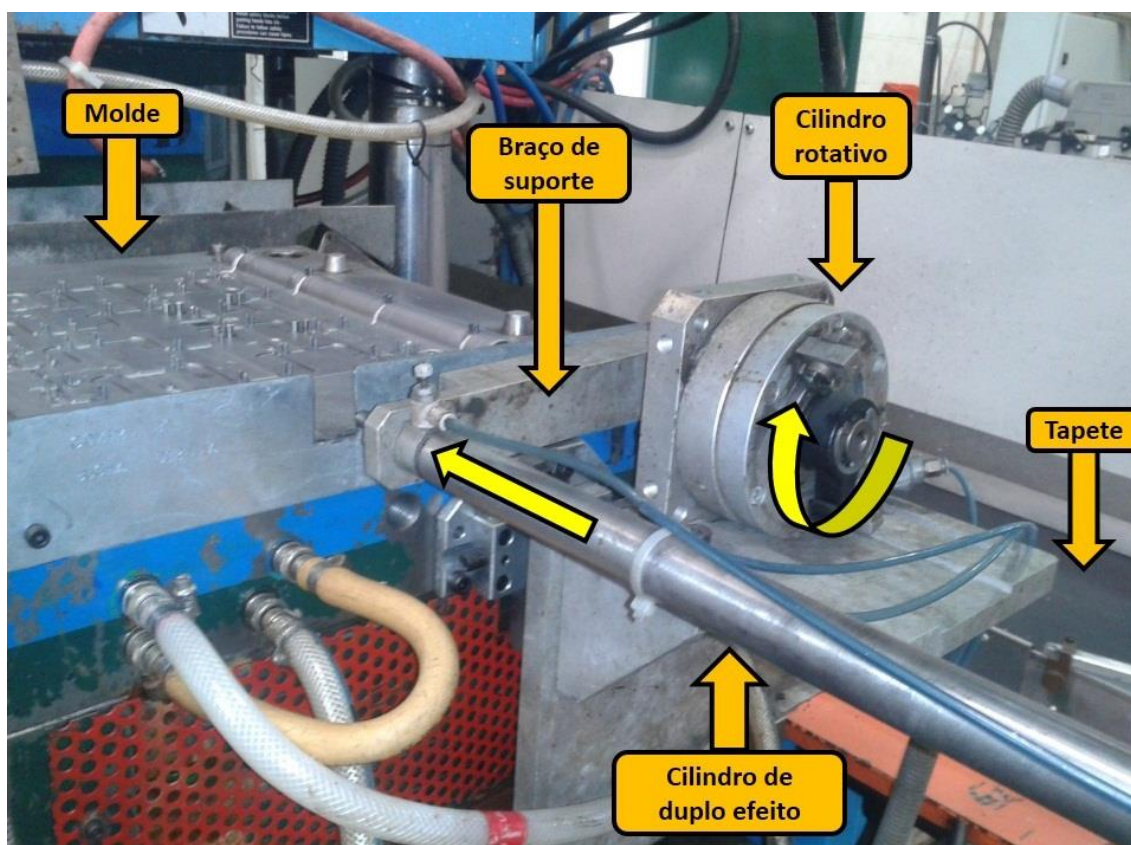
Componentes e movimentos da extração por cilindro pneumático rotativo.
